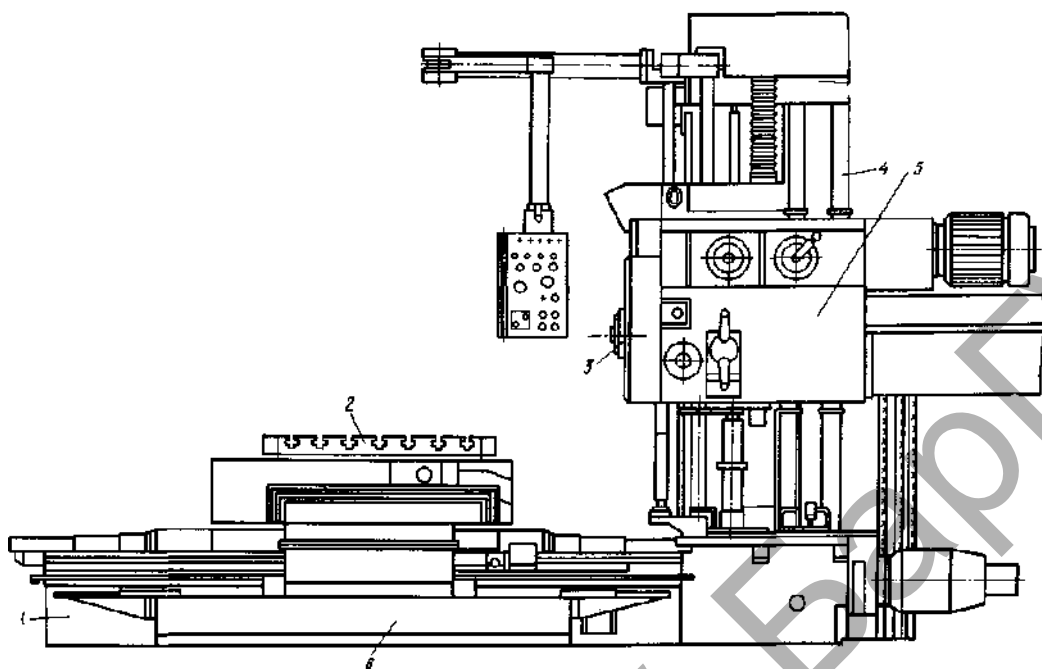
Горизонтально-расточной станок модели 2А622Ф4
